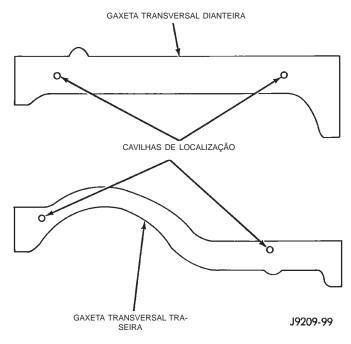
Gaxetas Transversais e Cavilhas de Localização
